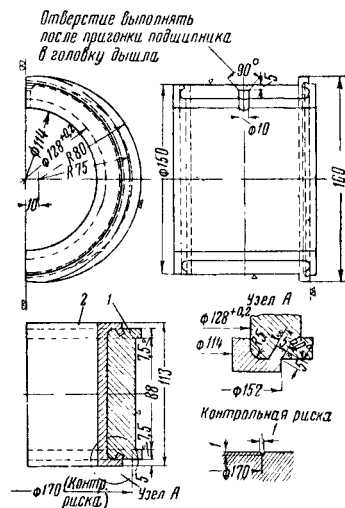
Разъемный подшипник задней головки ведущего дышла с бронзовой армировкой паровоза ЭМ
